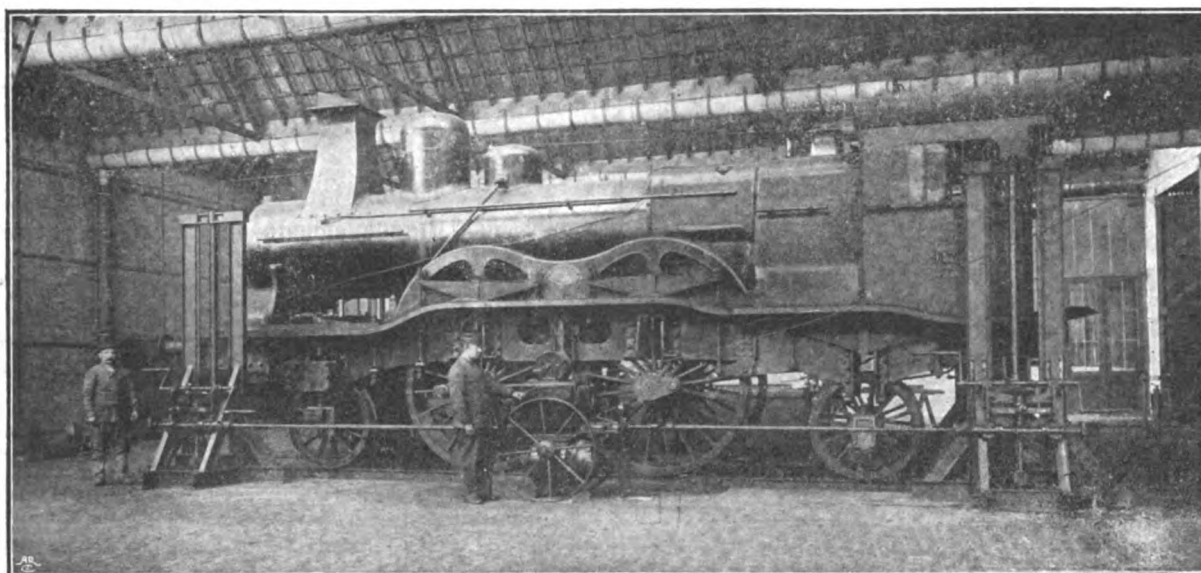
Cavalletti Schlesinger - Sollevamento di una locomotiva.
